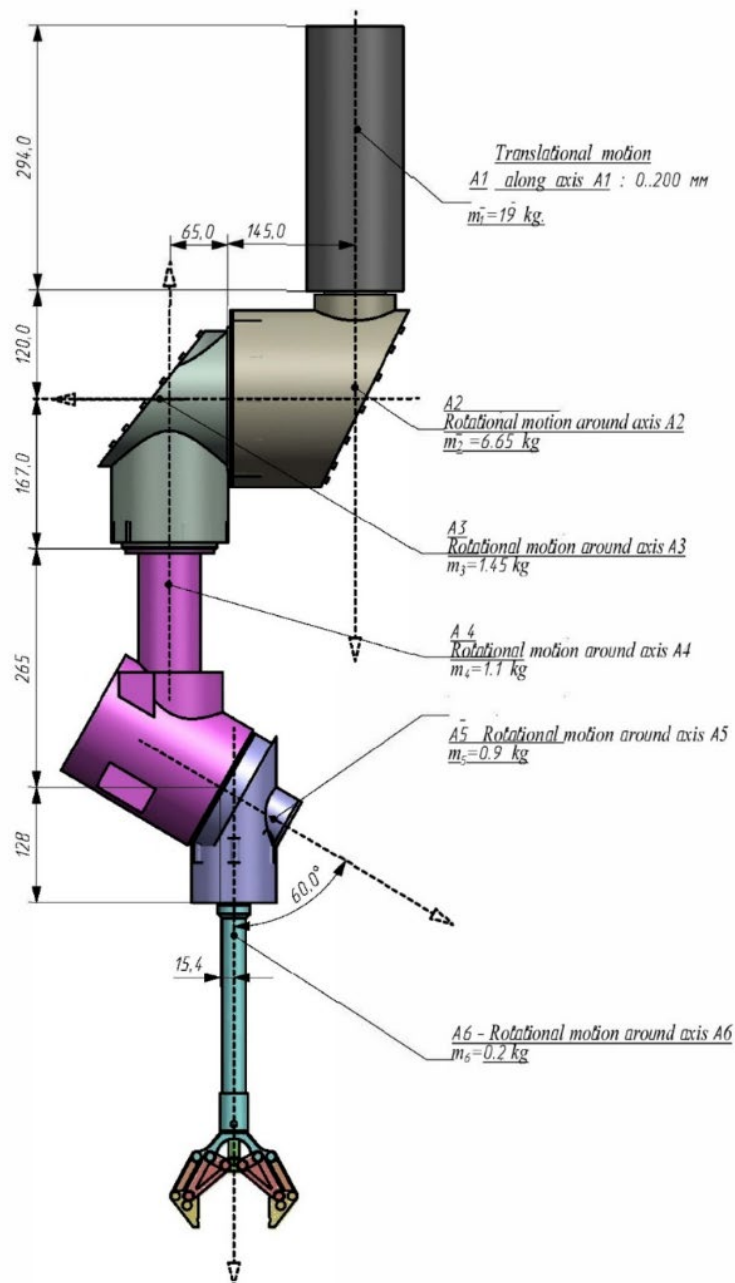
Схема шестизвенного робота-манипулятора
